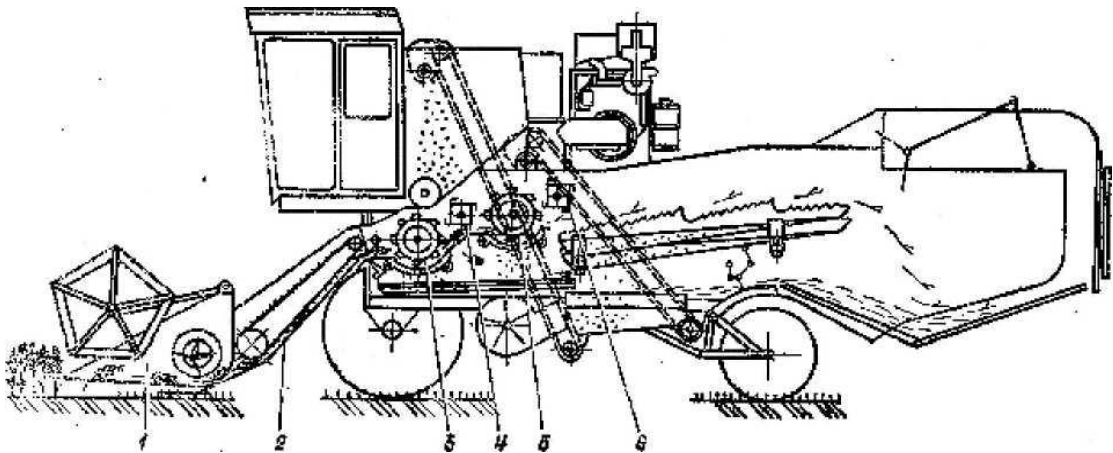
Схема технологічного процесу роботи двобарабанного комбайна: 1 – корпус жатки; 2 – корпус похилої камери; 3 – перший барабан; 4 – проміжний бітер; 5 – другий барабан; 6 – відбійний бітер.
